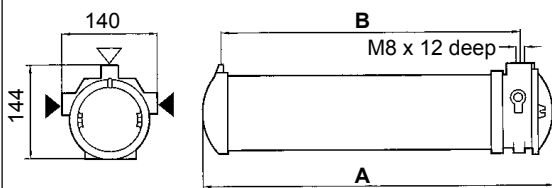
Dimensiones y peso / Dimensions and weight / . Abmessungen und Gewichte
